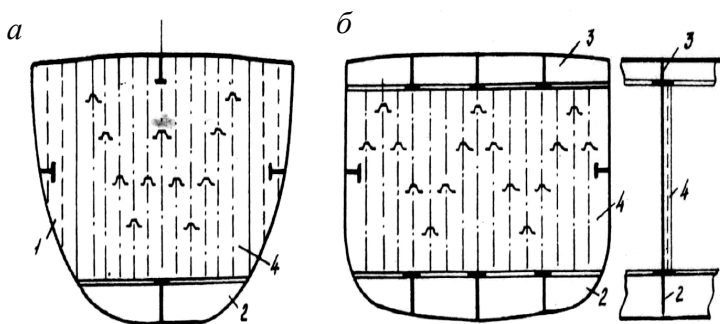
Крепление гофрированных переборок к корпусу:
